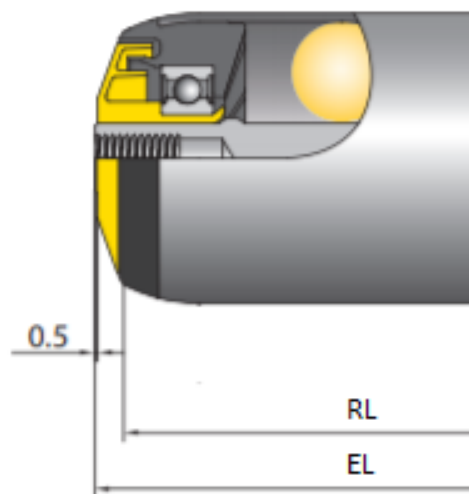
Váleček Roller Drive EC310 - pravá část [22]
